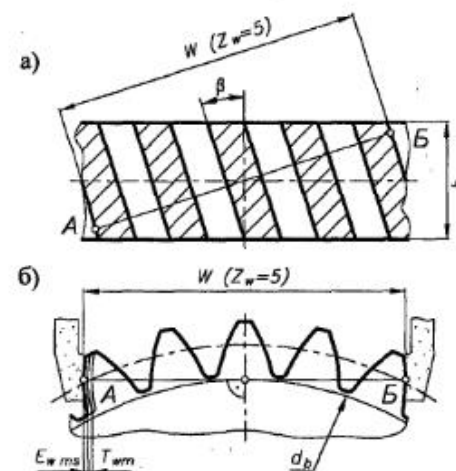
Схема замера длины общей нормали W при числе охватываемых зубьев $Z_w = 5$ для цилиндрических колес:
